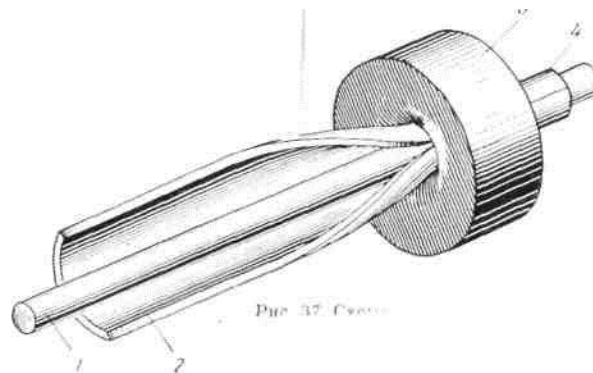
Схема процесу отримання біметалічного дроту сверткою смуги біля сердечника: 1 - сердечник; 2 - смуга, що згортається; 3 - волока; 4 - біметалічний дріт.
